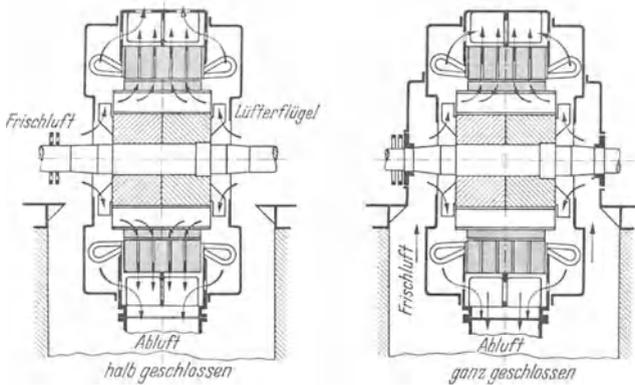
und 106. Bauformen von Schenkelpol-Synchronmaschinen mit Lüfterflügeln.
